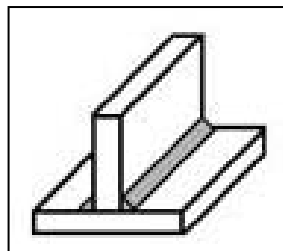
Típica unión en ángulo usando dos cordones de soldadura.
